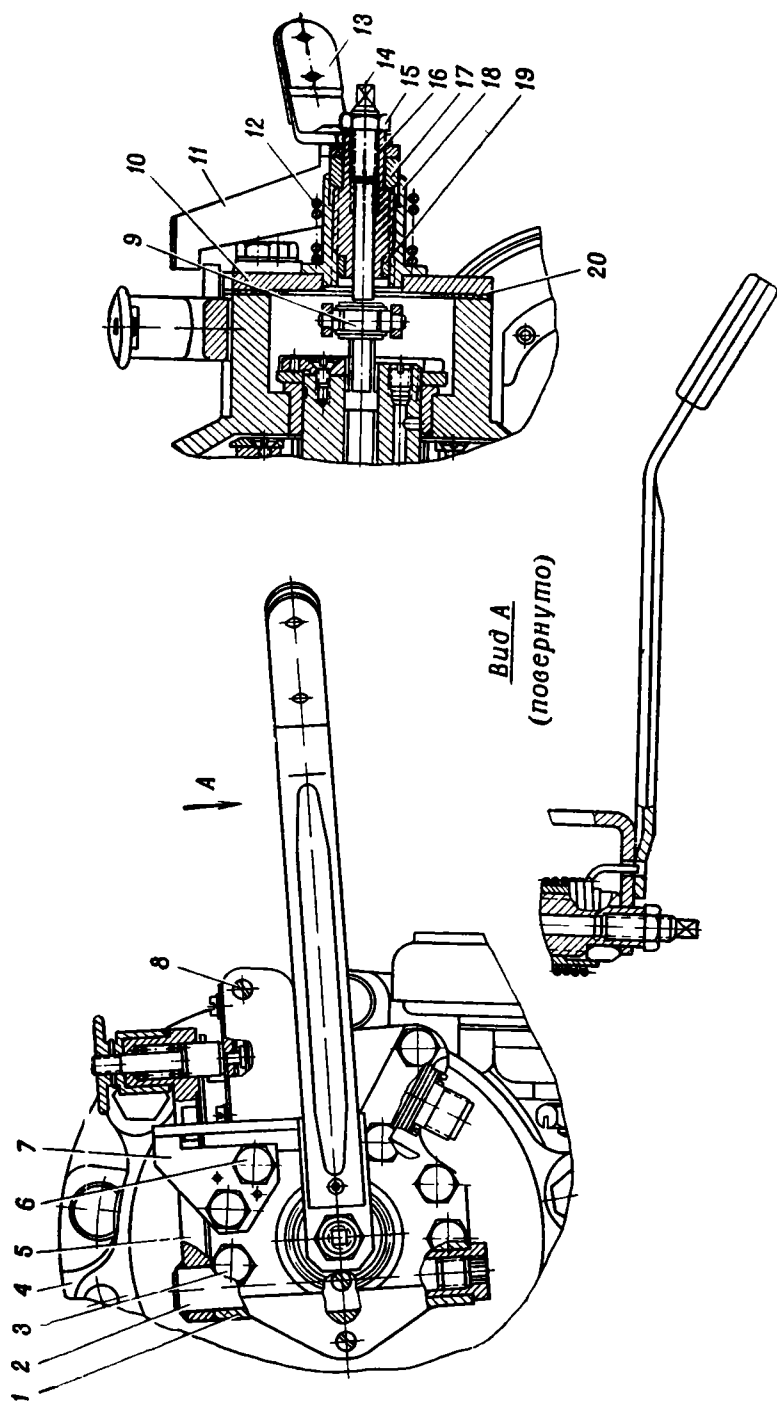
Установка механизма для снятия заклинивания на подъемном механизме:
